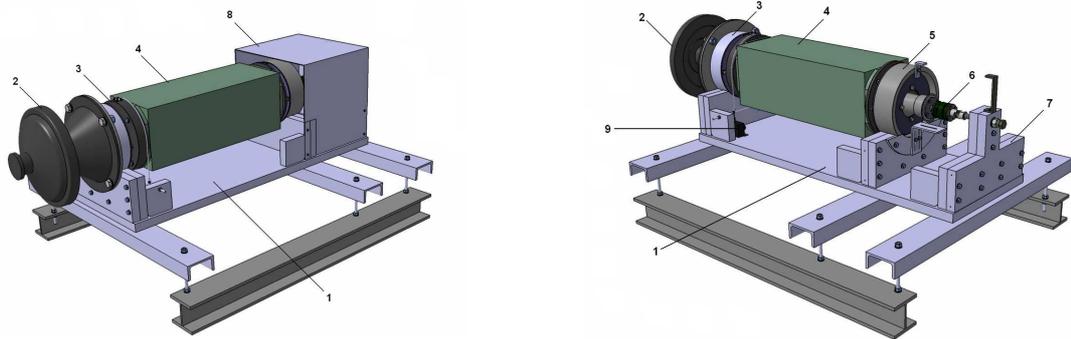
Gesamtaufbau der Motoraufhängung - *krp-004-00-00
